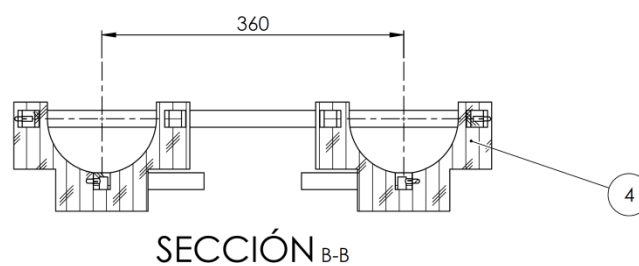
18: Vista de sección B-B del ensamble del espiral. Fuente: Elaboración propia.
